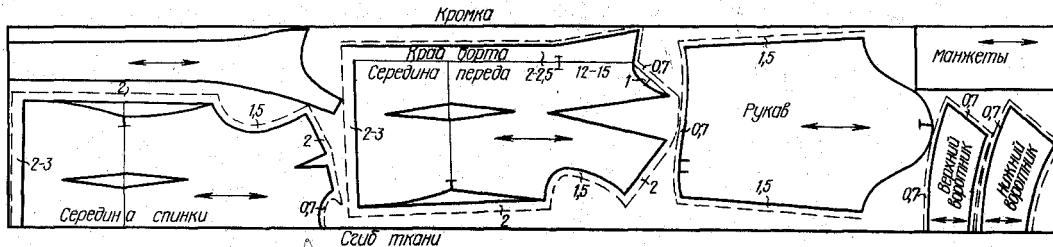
Раскладка выкроек на ткани и раскрой блузки с открытыми бортами
